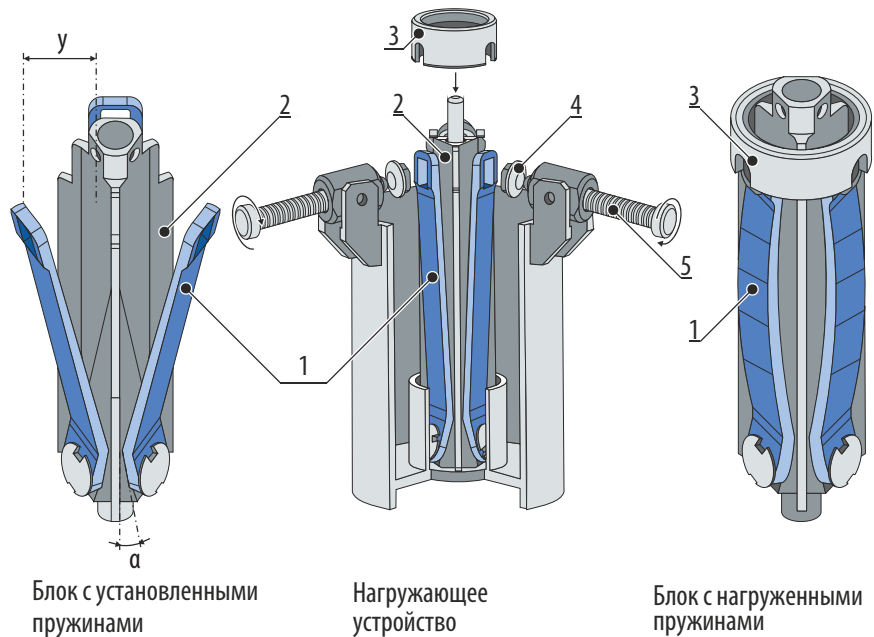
Схема нагружения пружин головки ТВС реактора PWR: 1 — пружины головки ТВС; 2 — корпус блока; 3 — фиксирующее кольцо; 4 — шайба; 5 — нагружающие винты
